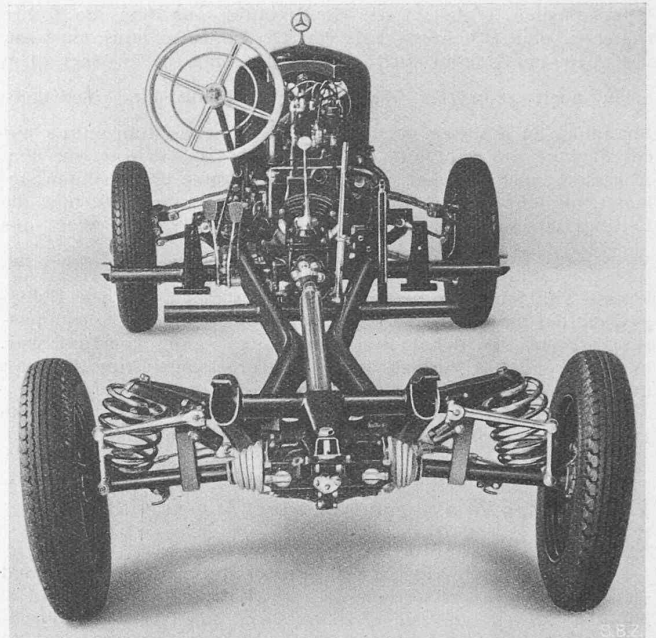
Chassis mit Einzelfederung aller vier Räder (Vollschwingachs-Chassis Mercedes-Benz 170 V, 9 PS). Rahmen modernster Ausführung, in X-Form geschweisste Träger von rechteckigem Profil. Vorn zwei übereinanderliegende Blattfedern, hinten Pendelachsen mit Spiralfedern
